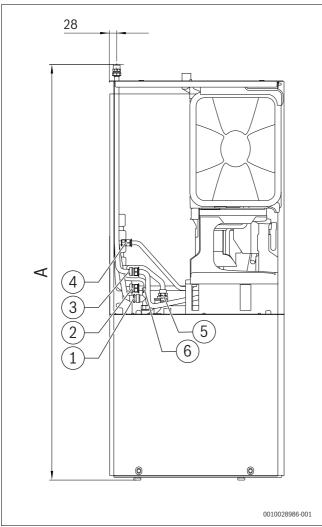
Vue côté arrière (dimensions en mm) : accessoire CS 10 FR-5300 monté sur le côté droit
